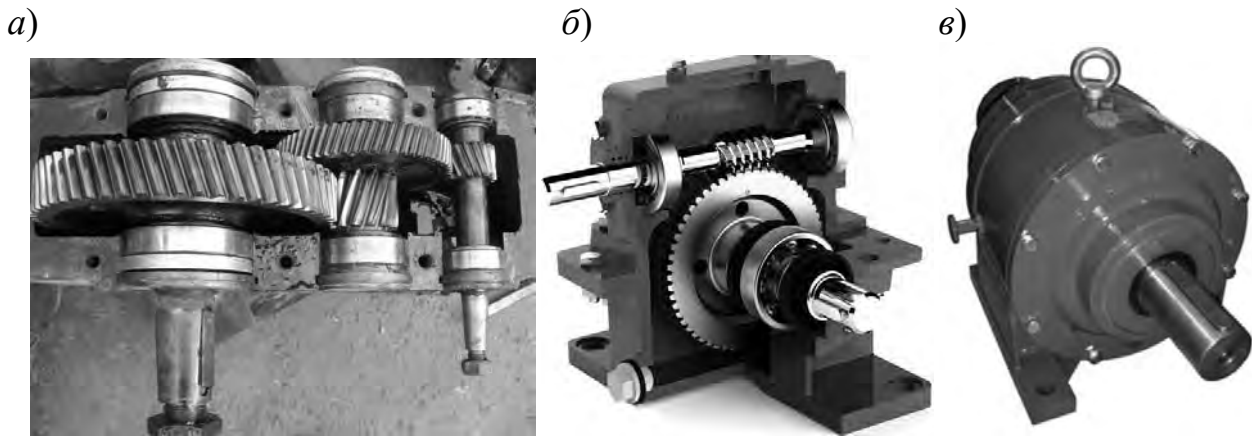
Общий вид редуктора: *а* – двухступенчатый цилиндрический со снятой крышкой; *б* – червячный; *в* – планетарный
